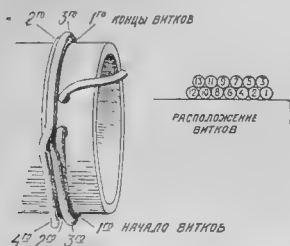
Способ намотки и расположение витков двуслойной катушки.
